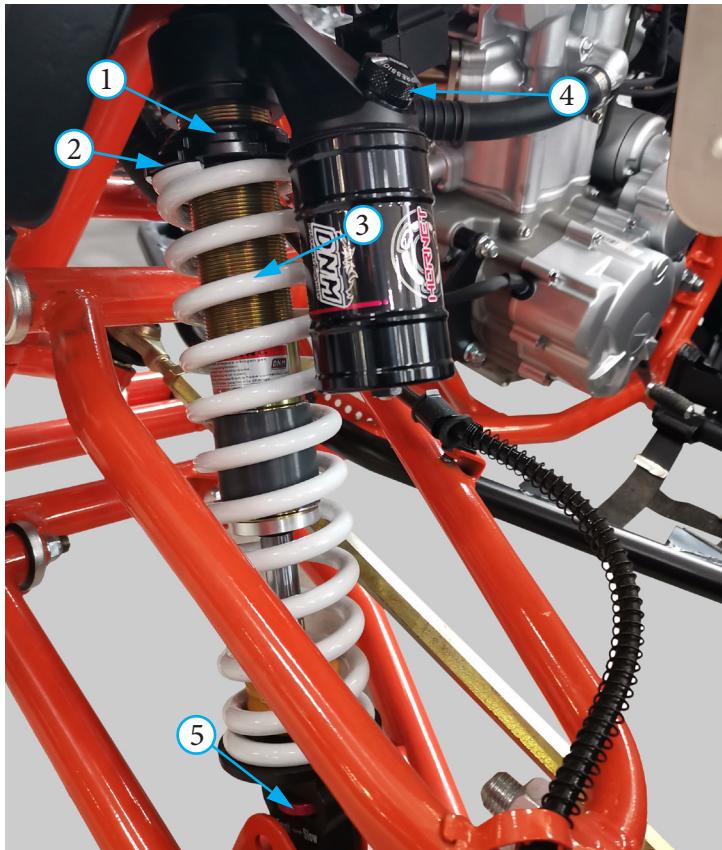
Регулировка преднатяга пружины переднего амортизатора и системы демпфирования: 1 – гайка контровочная; 2 – гайка регулировочная; 3 – пружина; 4 – гайка регулировки сжатия; 5 – гайка регулировки отбоя
